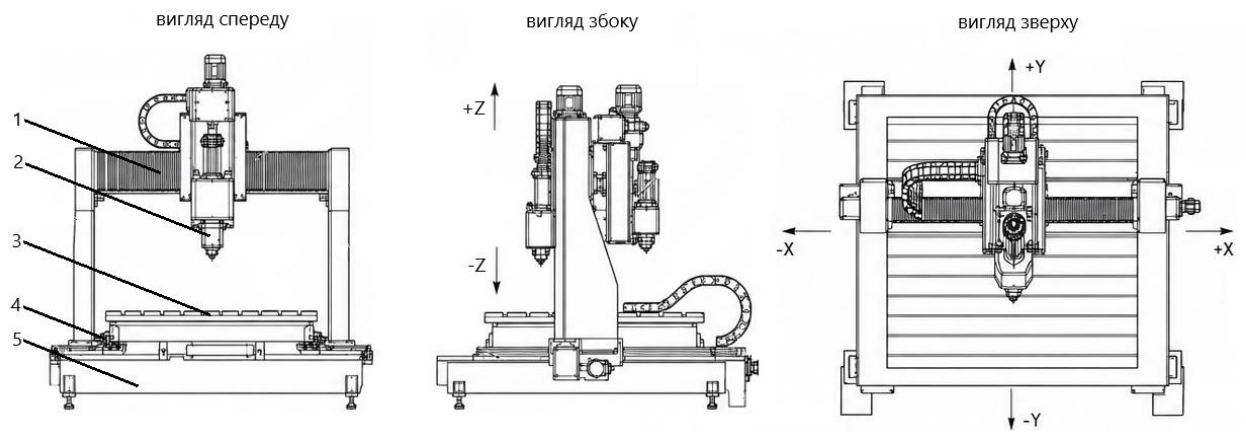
Конструктивна схема три координатного фрезерного верстата портального типу з позначенням основних вузлів
